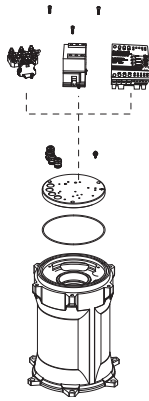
Montage du support de la plaque à bornes (J 205)
